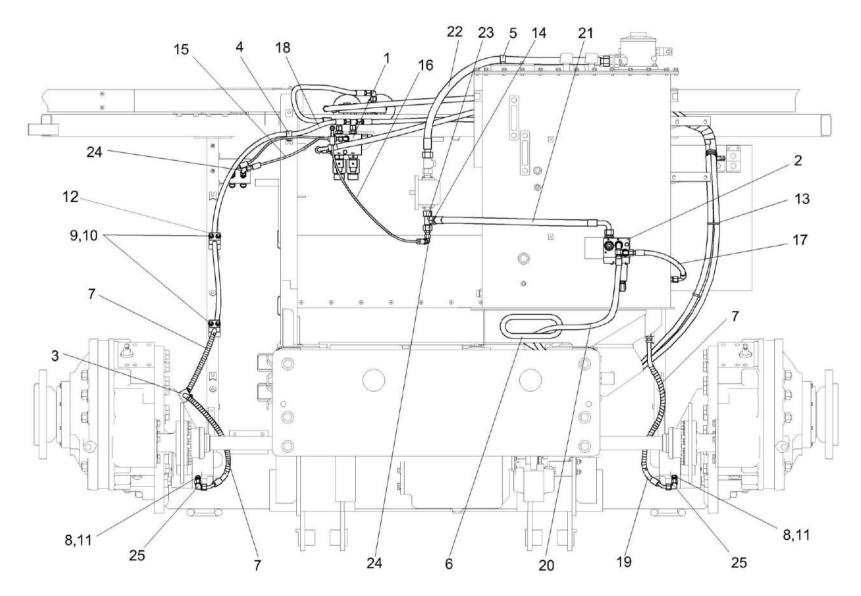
Гидросистема привода стояночного тормоза КВК-2-0606000А (вид спереди)
